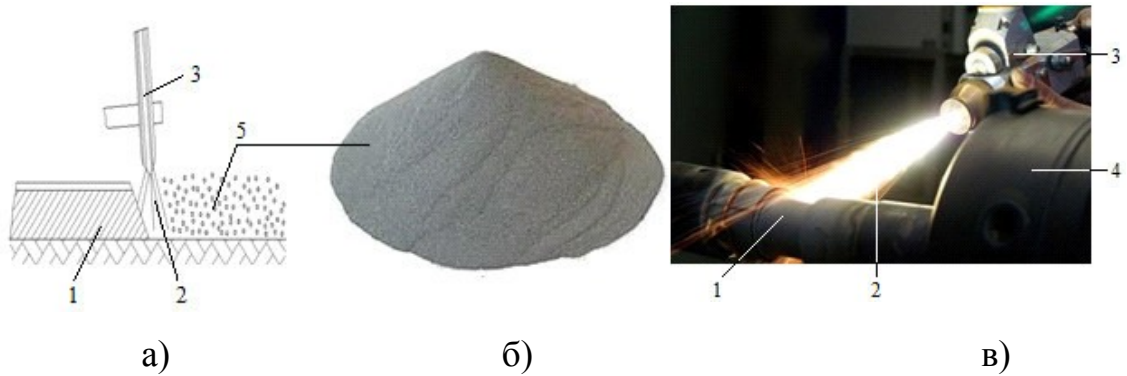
Наплавлення порошкоподібними сплавами:
